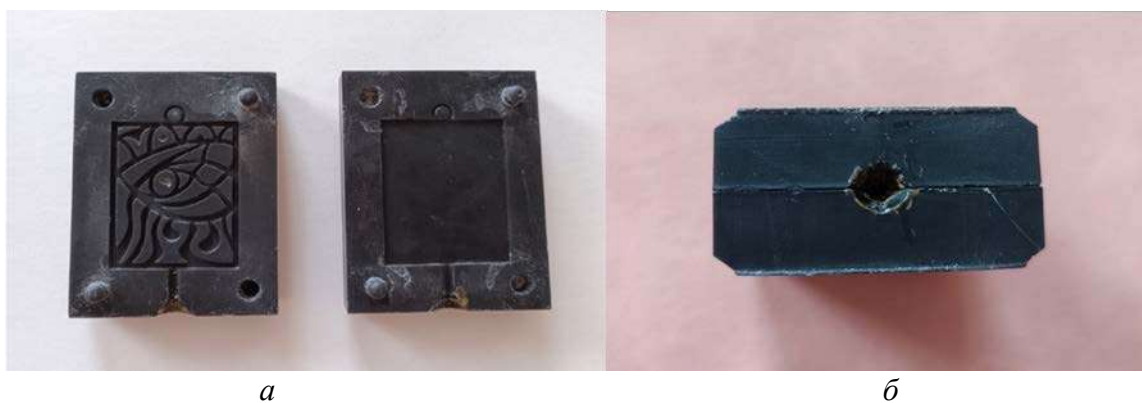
Напечатанные две половинки пресс-формы: а – рабочая поверхность пресс-формы, б – собранная пресс-форма
